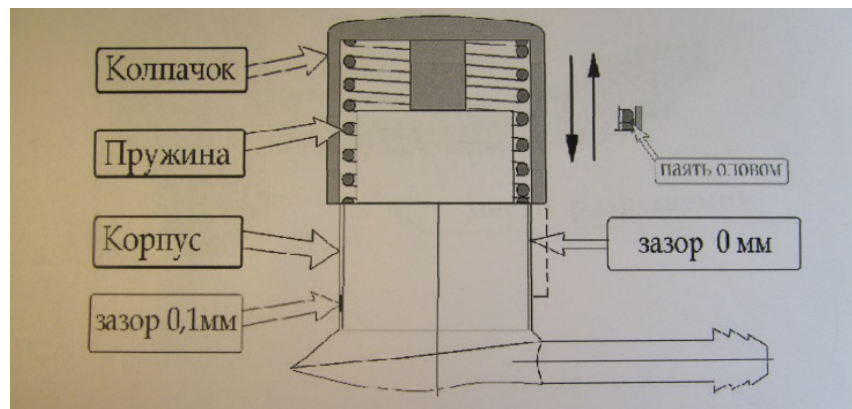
Для профилактики заклинивания колпачка в нижнем положении увеличен зазор между внутренней поверхностью крышки колпачка и наружной поверхностью корпуса до 0,1 мм; кроме того, дистальный конец пружины колпачка (пружина обеспечивает возврат крышки клапана в верхнее положение после прекращения надавливания) припаивается к крышке колпачка
